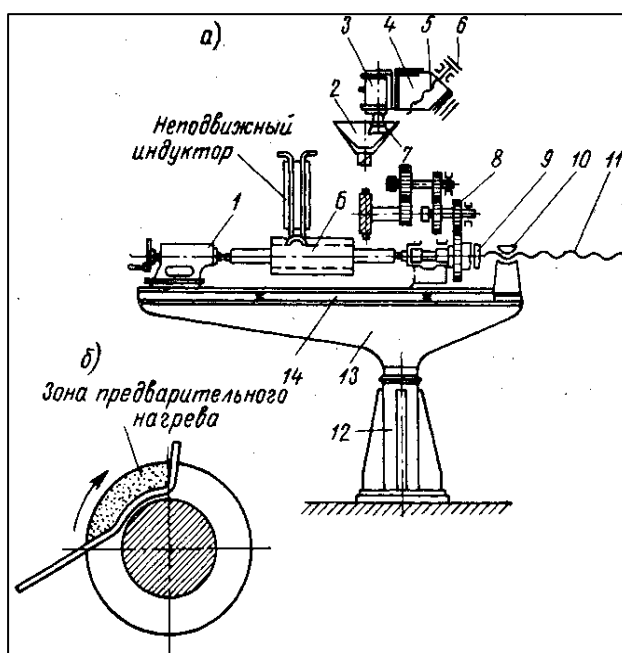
Схема станка для закалки червяков (а) и схема нагрева витка червяка (б).
